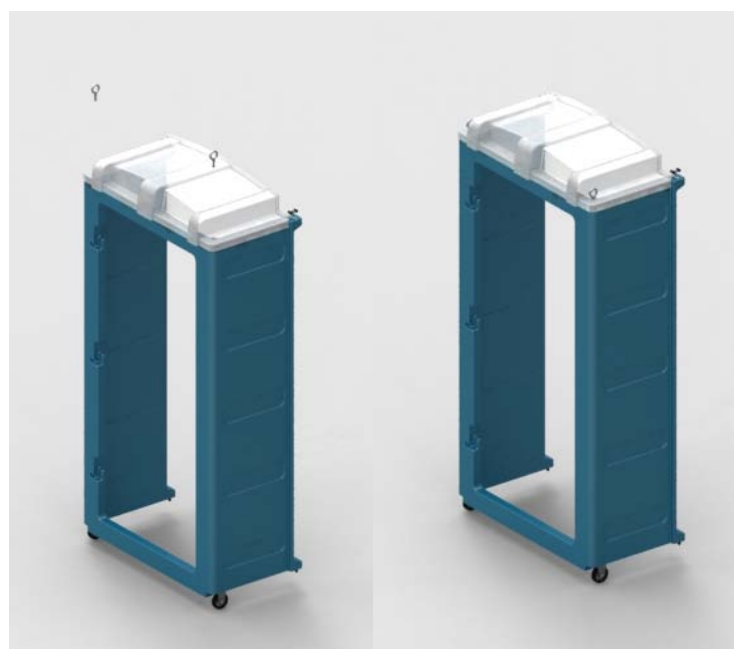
Assemblaggio del kit di sollevamento anteriore
